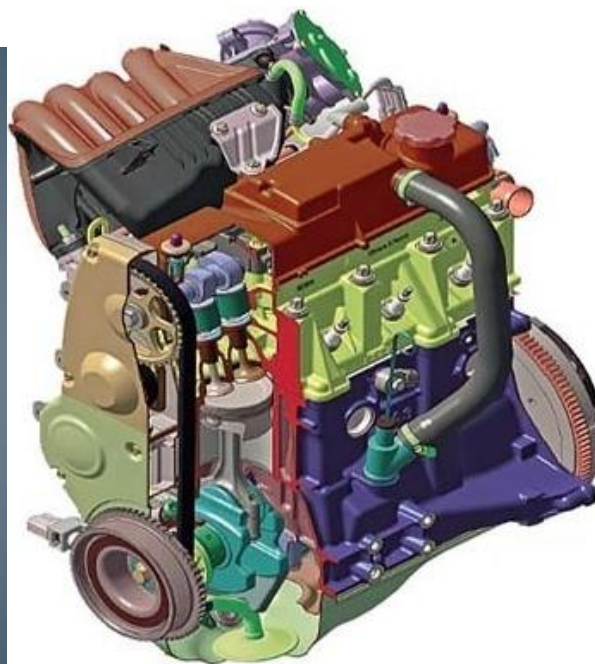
Общий вид двигателя ВАЗ-11186, взятого как базовый для расчета
